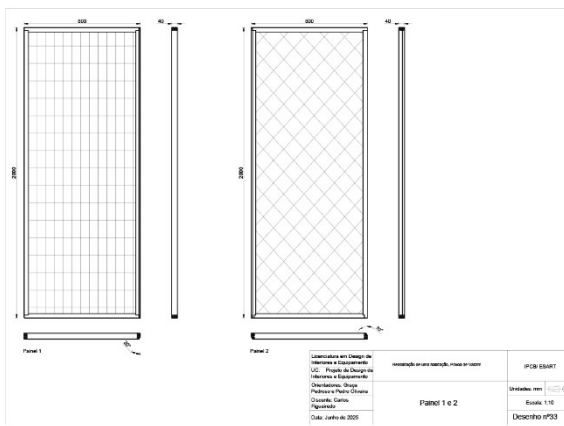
Painéis 1 e 2. Fonte: Autor.
